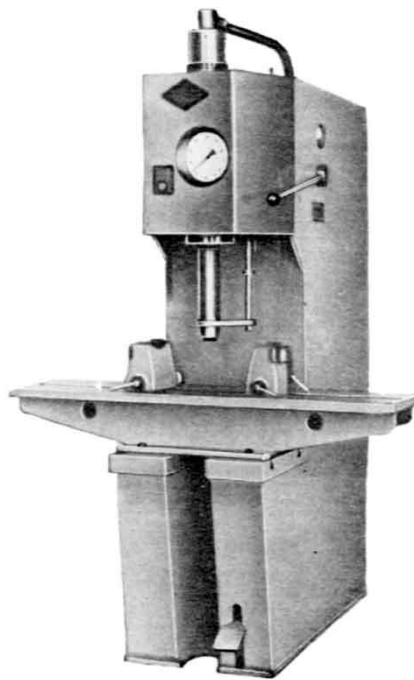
Гидравлический одностоечный пресс П6320
